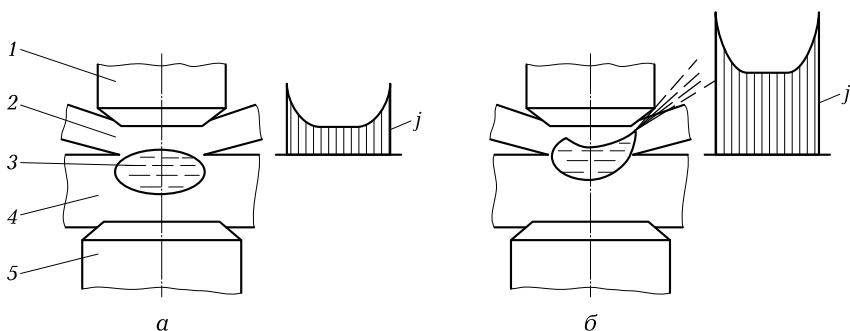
Зона расплавления и плотность тока  $j$  при сварке деталей неравной толщины:
